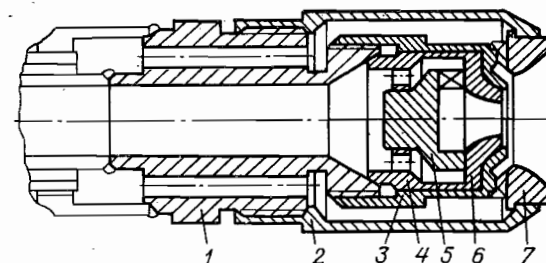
Головка паромеханической форсунки «Титан-М» [36].
